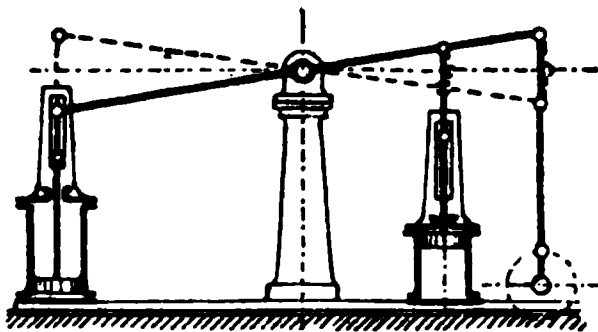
Woolfsche Balanciermaschine mit entgegengesetzt gerichtetem Kolbenlauf, System Mac Naught.
